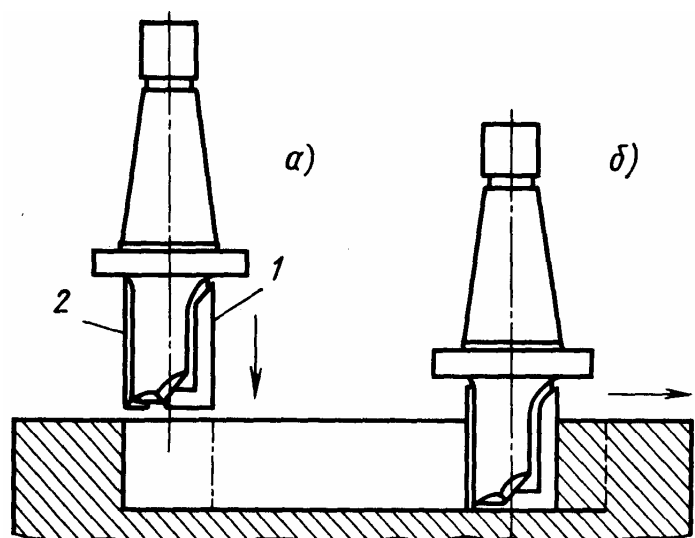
Обробка закритого шпонкового паза свердлопазовою фрезою фірми „Вальтер” (ФРН)
